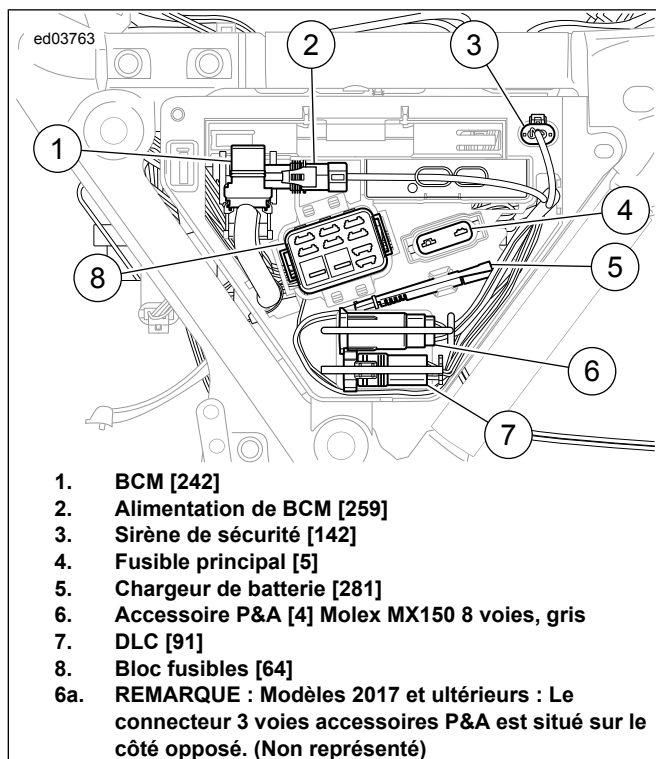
2014 à 2016 : Couvercle latéral gauche
